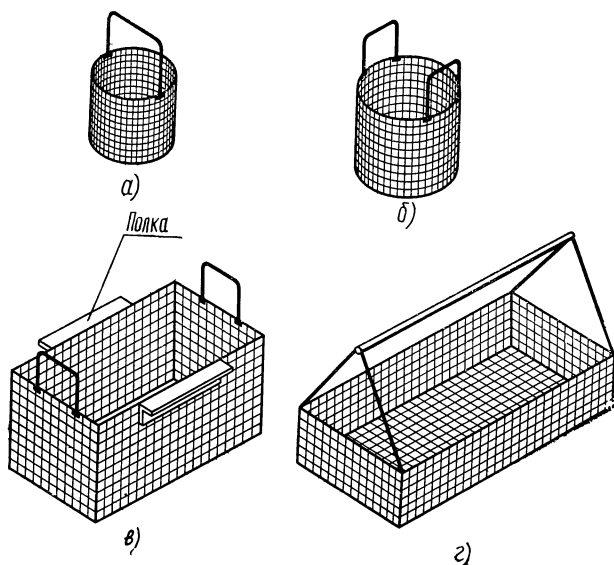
Универсальные вспомогательные приспособления для ультразвуковой очистки:
